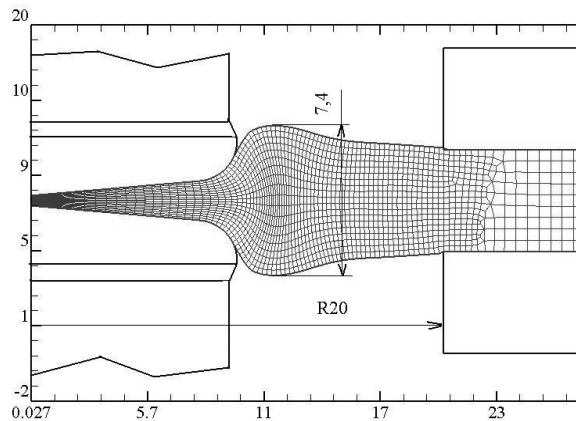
Форма і розміри заготовки в міліметрах після видавлювання
